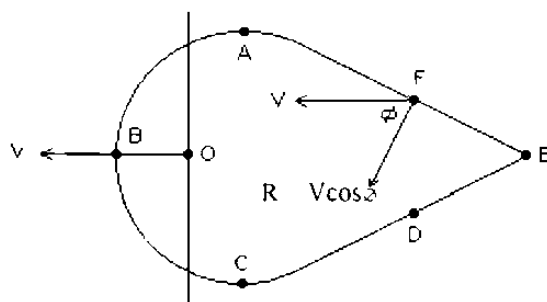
Representación esquemática de una pileta líquida de soldadura en forma de gota
